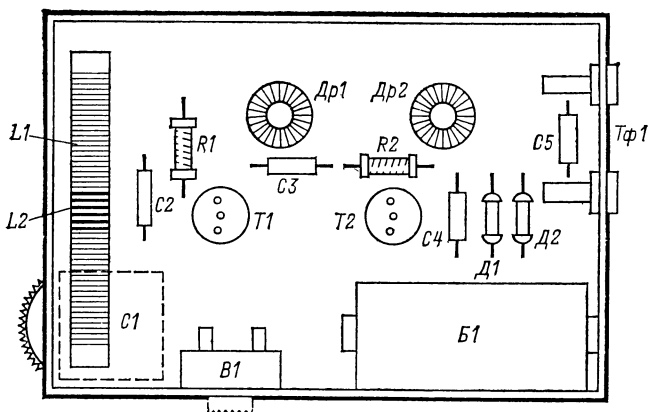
Расположение деталей в корпусе двухтранзисторного приемника
